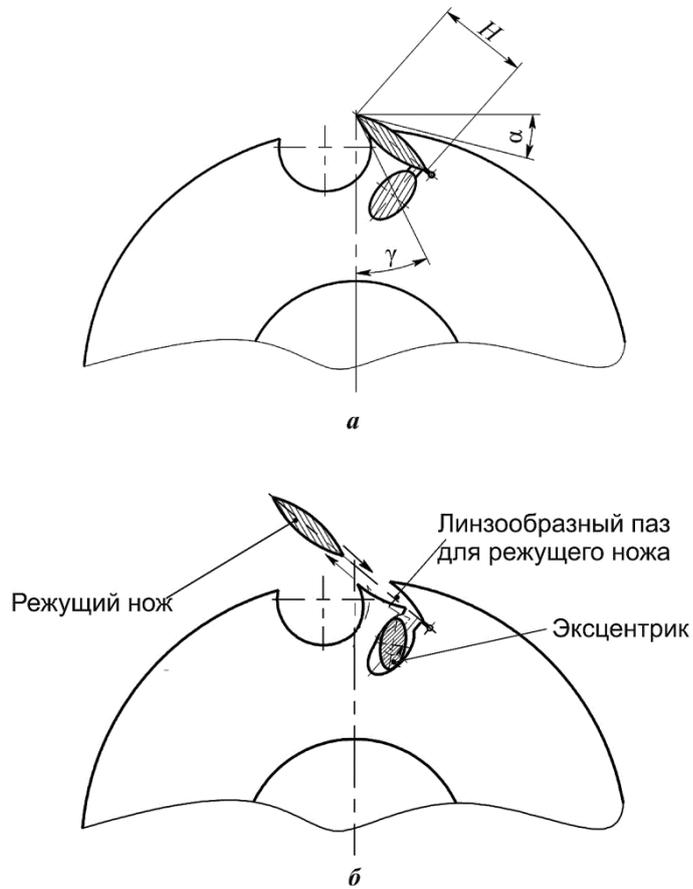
Узел крепления линзообразного режущего элемента (а) и схема крепления ножей с помощью эксцентрика (б)
